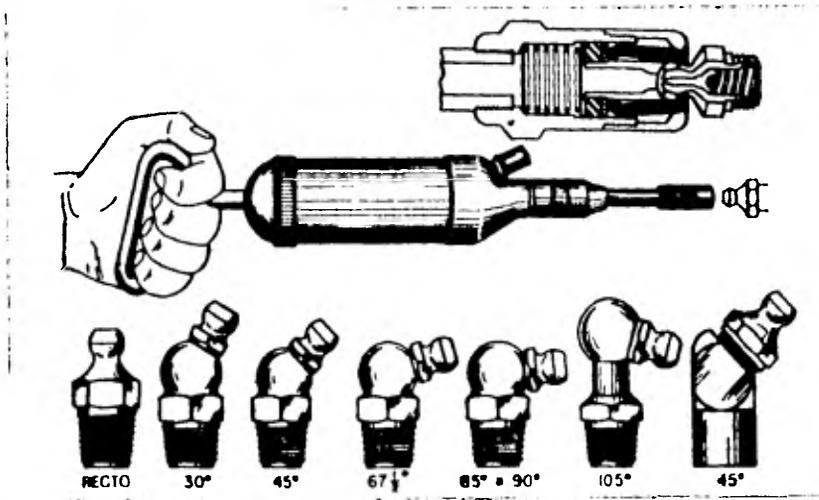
Pistola de engrase a mano y engrasadores mostrando el corte de la boquilla.
